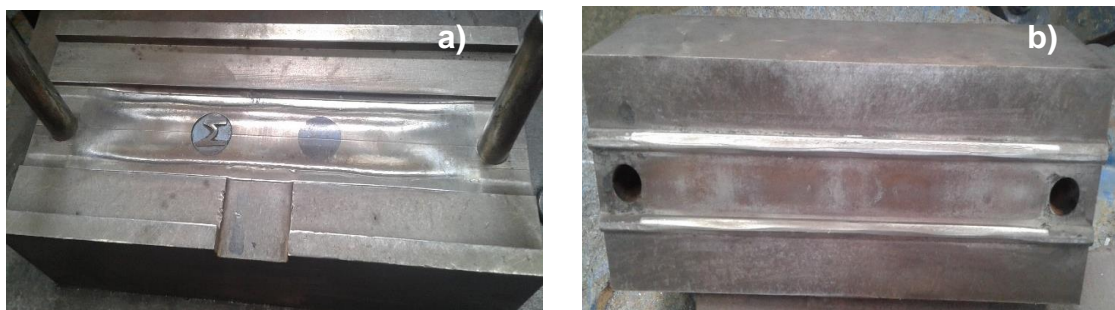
Matriz. a) Parte inferior, b) Parte superior
